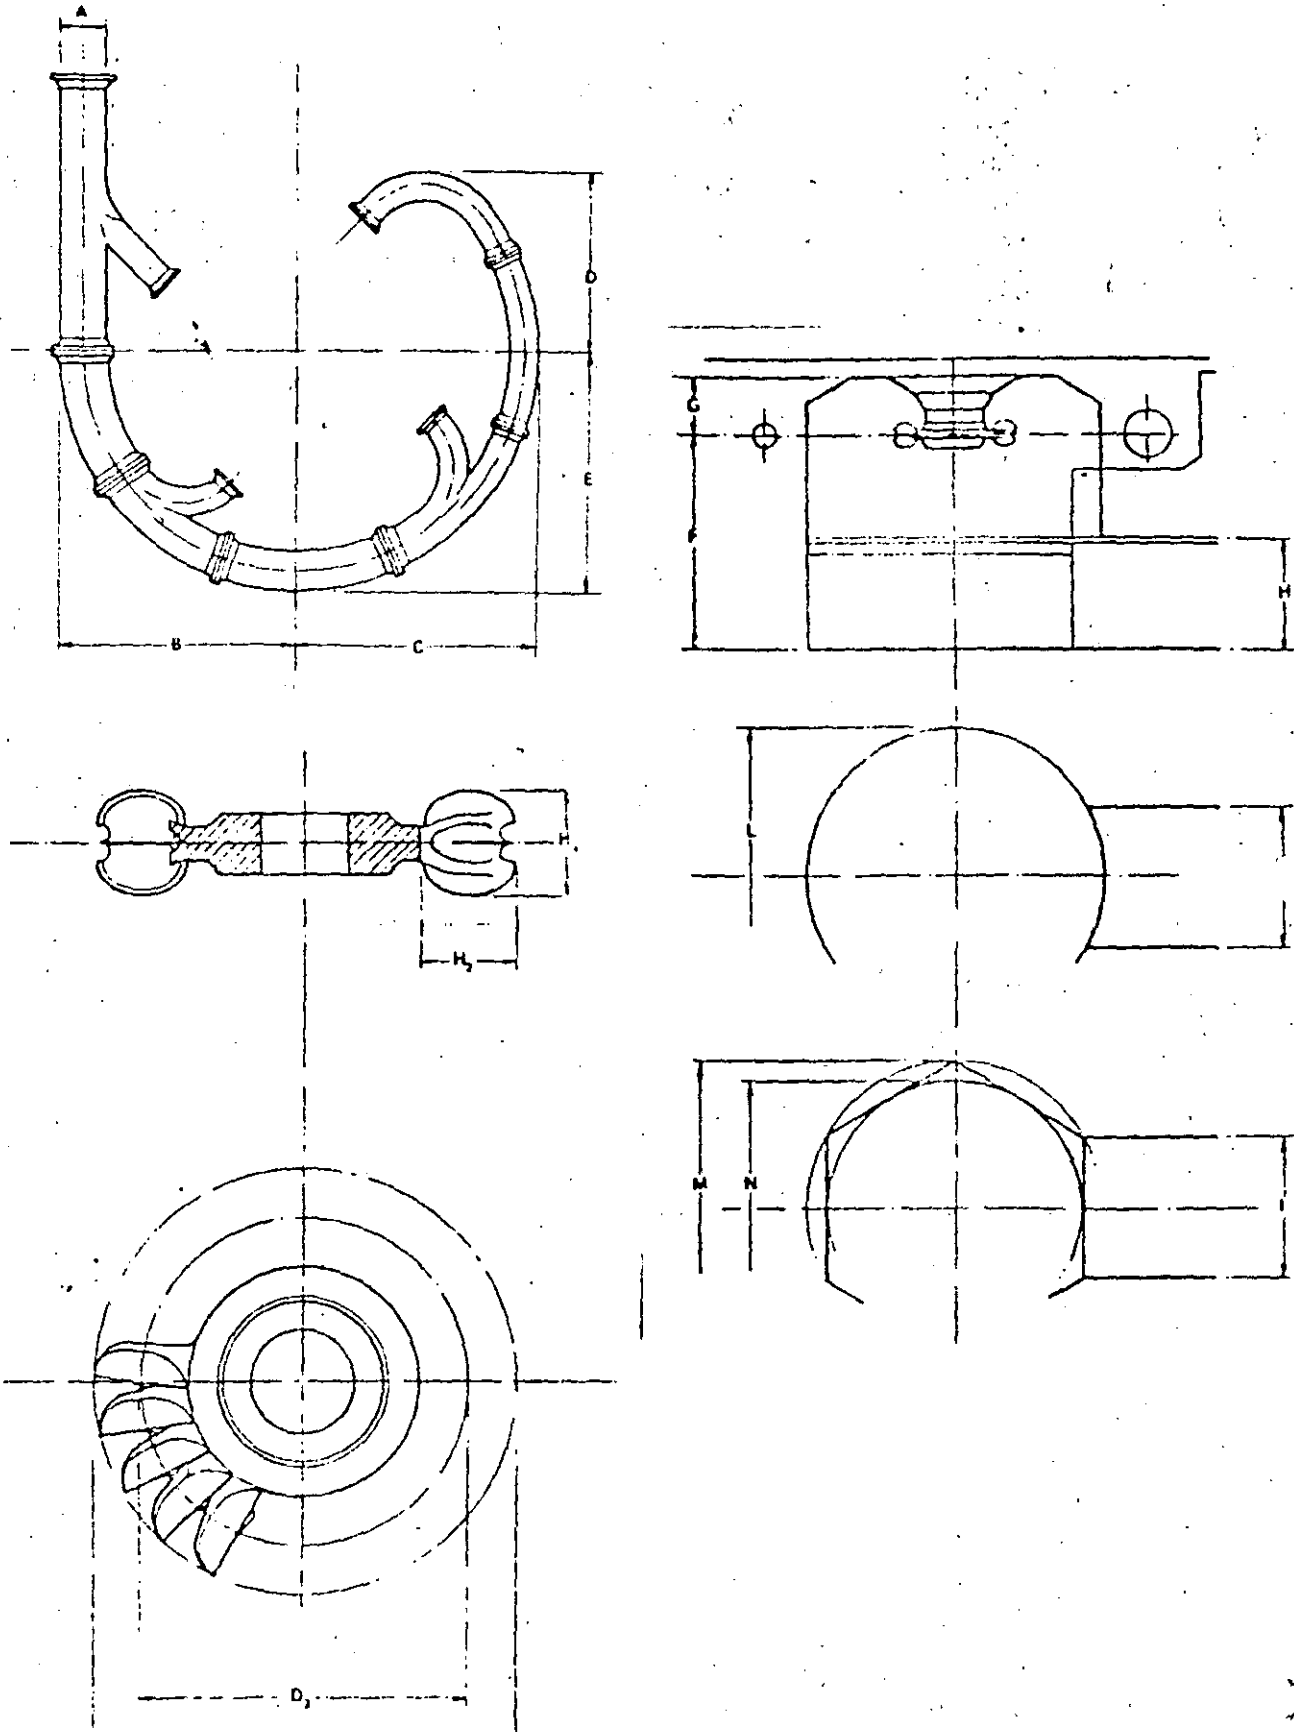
DIMENSIONES DE TURBINAS PELTON
